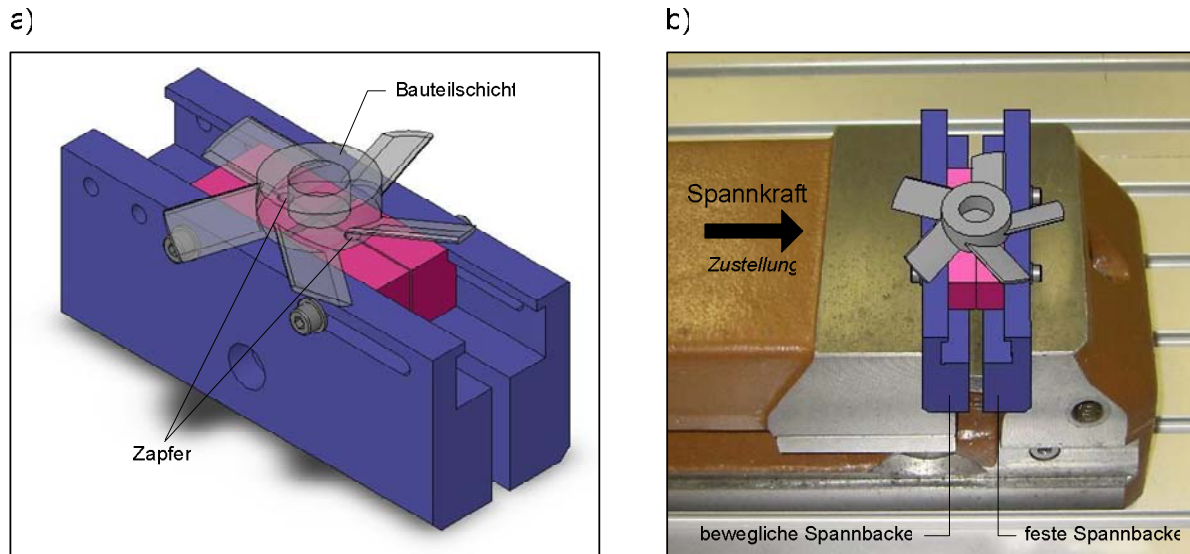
a) Aufnahme einer Bauteilschicht mit Zapfen b) Gesamtdarstellung: Maschinenschraubstock und Vorrichtung
